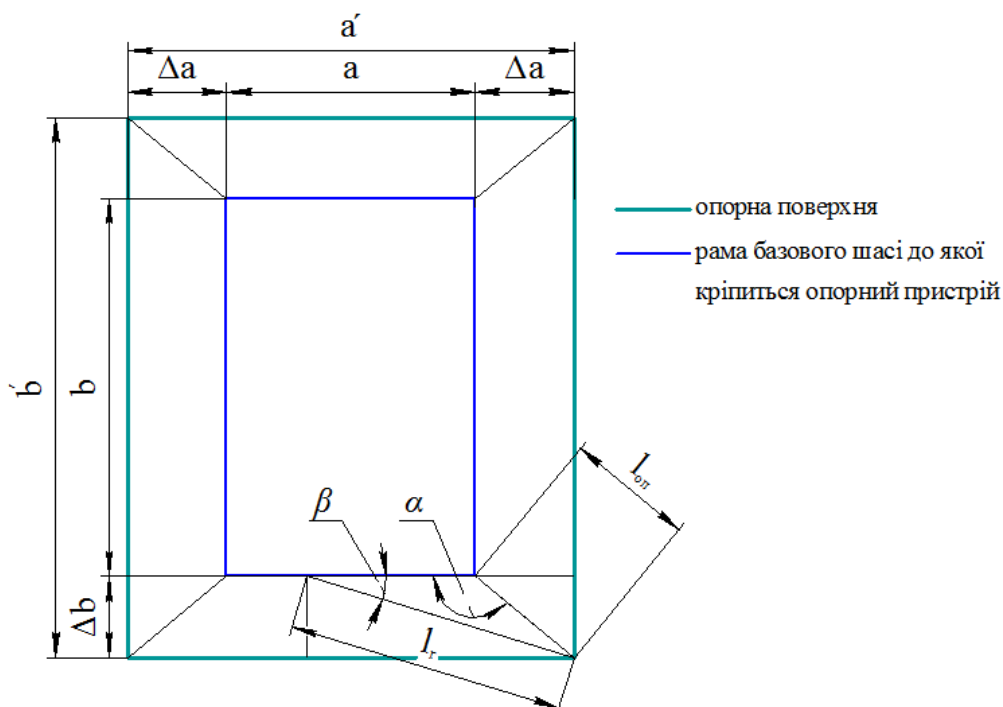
Схема для визначення площі опорного пристрою з механізмом регулювання бази машини
